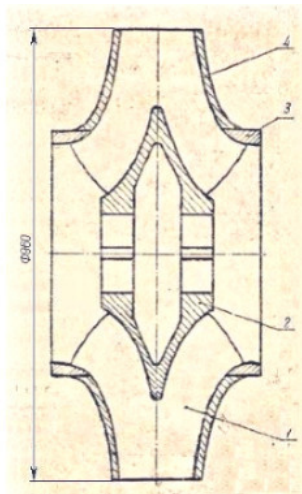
Рабочее колесо сварной конструкции центробежного насоса двустороннего входа 24НДс
